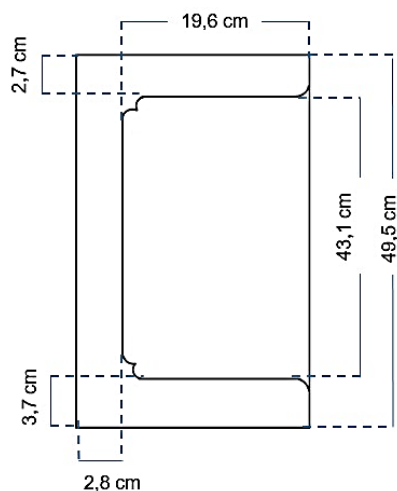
Esquema de las planchas de madera chapeada para las puertas
